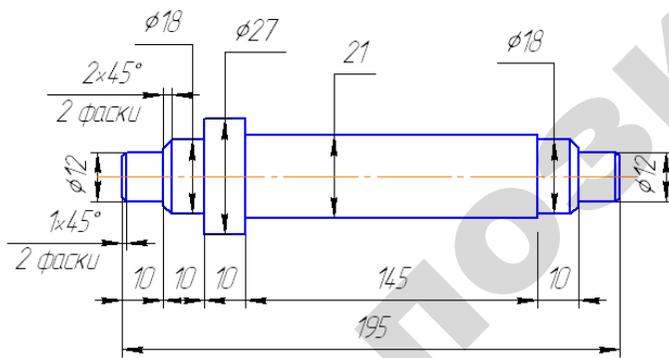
Оправка для выпрессовки и запрессовки гнезда перепускного клапана
